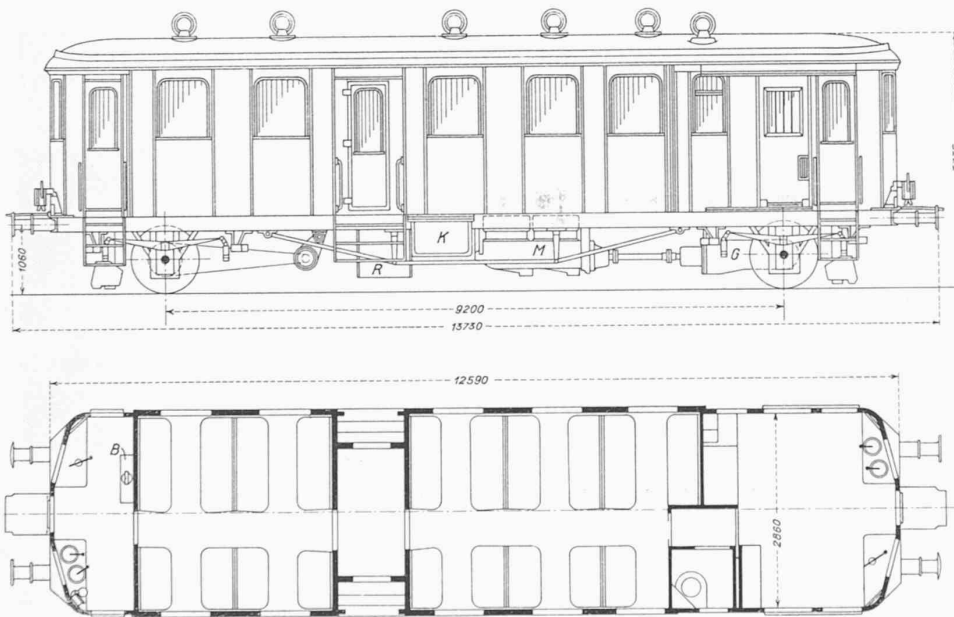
Aufriss und Grundriss des Wagens Nr. 9912. — Masstab 1 : 100.
